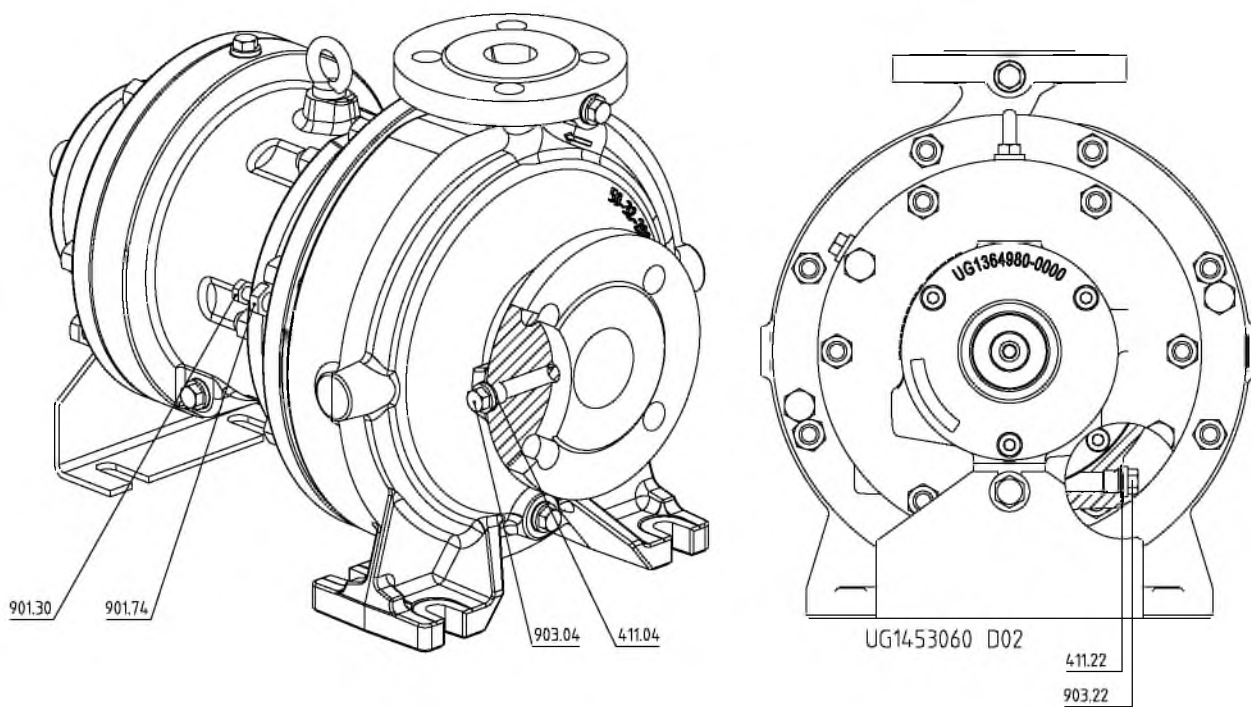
Крепление крышки корпуса с напорной стороны на корпусе насоса для исполнения с привинчиваемой крышкой
